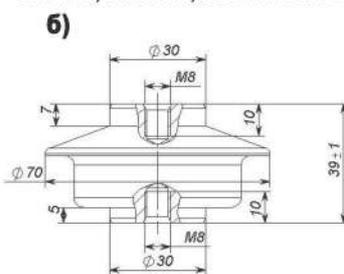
Габаритно-присоединительные размеры ОПНп класса напряжения 0,4
